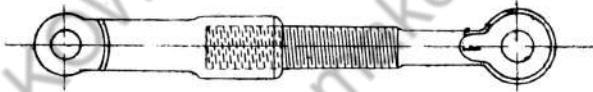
Тяга, соединяющая педаль сцепления с рычагом валика выключения сцепления. Резьба служит для изменения длины тяги
